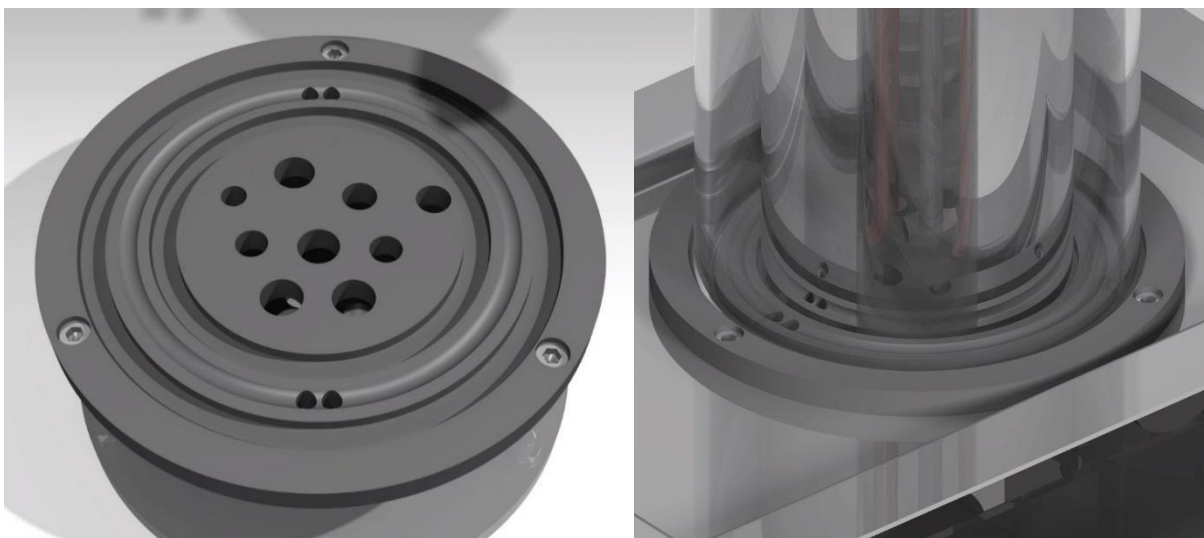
Gesamtansicht Boilerboden (links) und Bodenblech mit Boden und Boiler (rechts)
